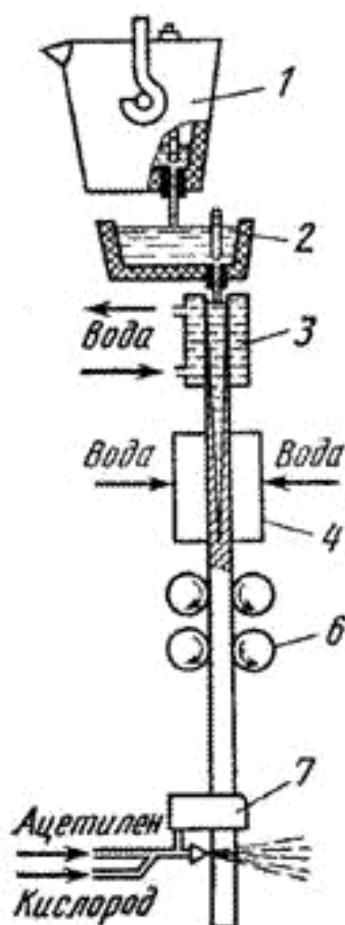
Схема непрерывной разливки металлов на металлургическом заводе
